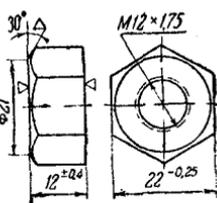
Дет. № 3036. Гайка к шпильке крепления кронштейна выхлопного патрубка и сектора заслонки подогрева
